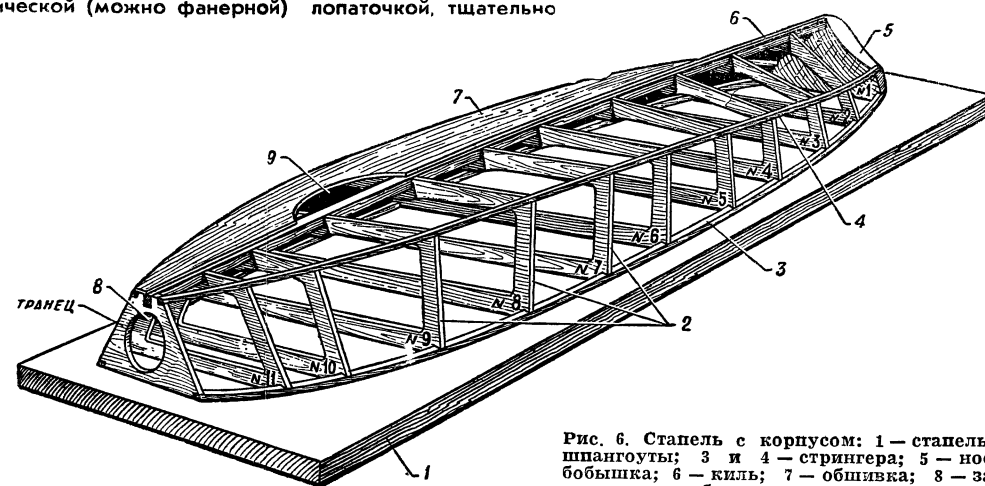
Стапель с корпусом: 1 — стапель; 2 — шпангоуты; 3 и 4 — стрингера; 5 — носовая бобышка; 6 — киль; 7 — обшивка; 8 — заднее отверстие трубы; 9 — входное отверстие трубы
